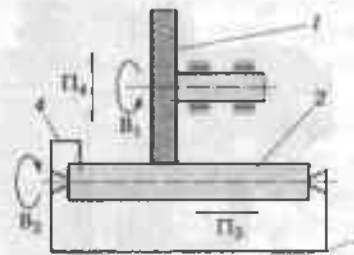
Схема обработки на центровом круглошлифовальном станке:
